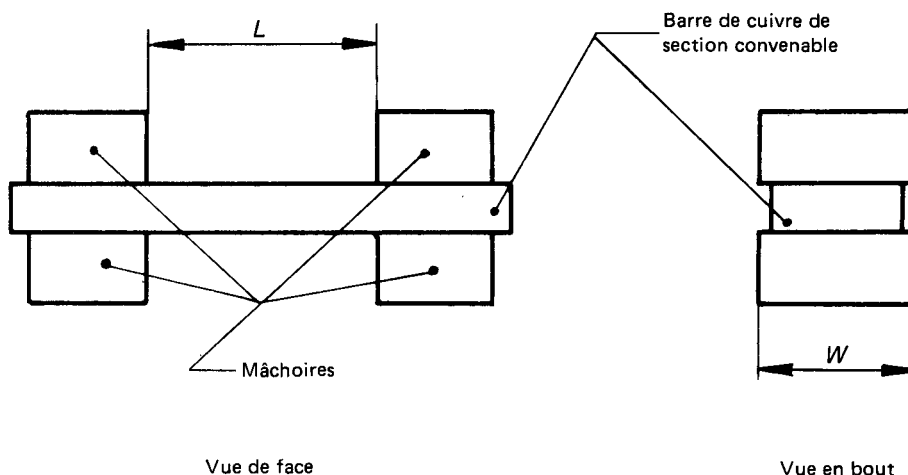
Barre pour mise en court-circuit de machine à souder en bout
